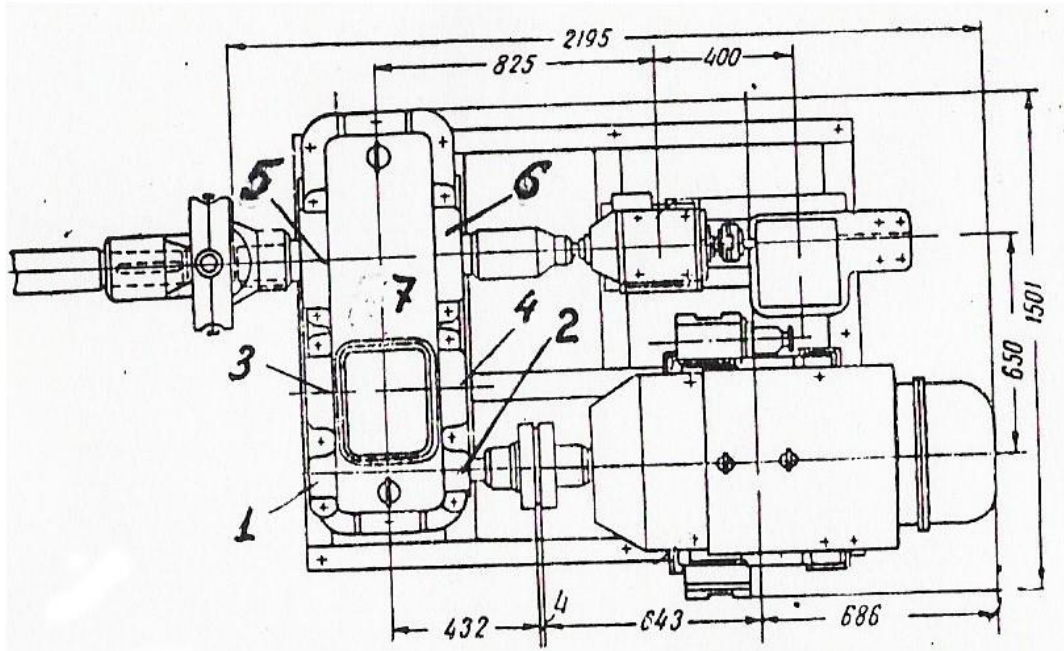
Карта змащення циліндричного редуктора приводу розподільника шихти, що обертається
